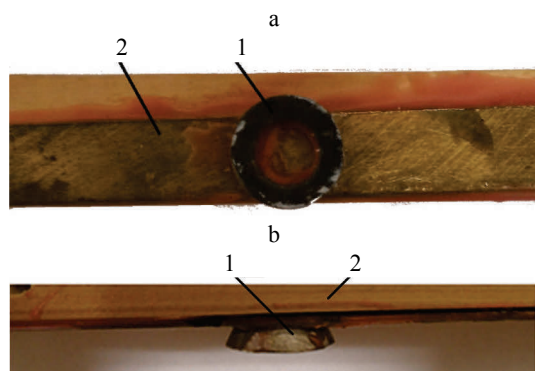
Фотография латунной пластины с закрепленной на ней шайбой: а – вид сверху; б – вид сбоку; 1 – шайба; 2 – пластина
